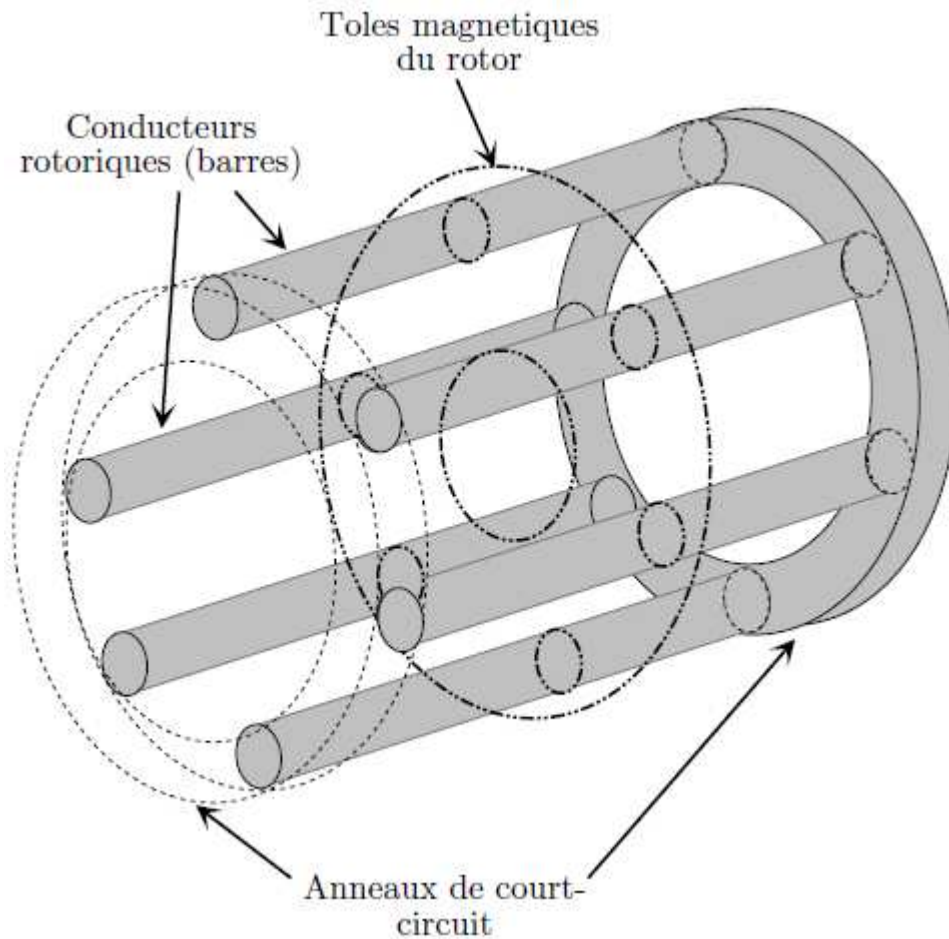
Représentation schématique d'un rotor à cage d'une machine asynchrone [2].
